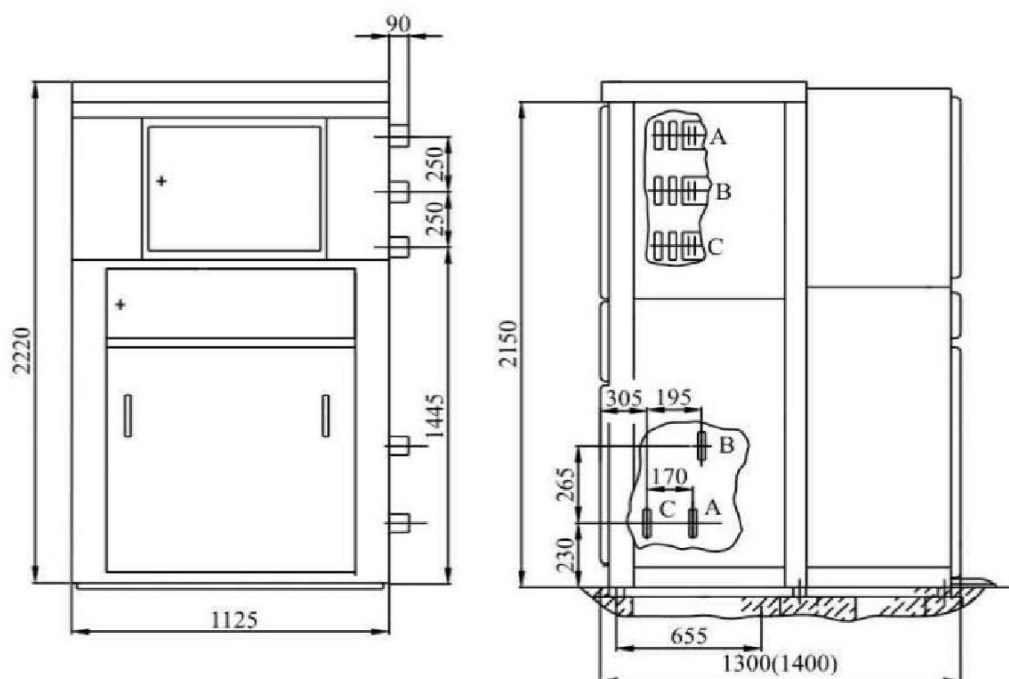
Габаритные, установочные и присоединительные размеры шкафов КРУ серии КМ-1ФМ на токи 2000...3150 А
